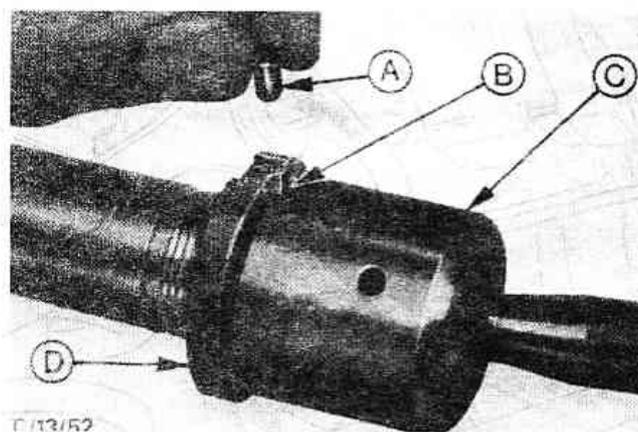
Установка стопора (А) в корпус шарового шарнира рулевой тяги (С) и контргайки (D) в новое отверстие (В) (Разд.30)
